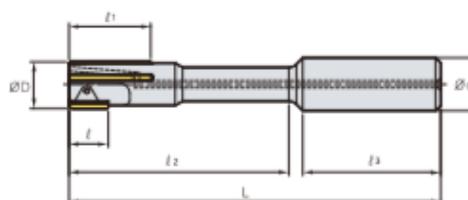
Дисковая фреза SPS 063-0305-10R
